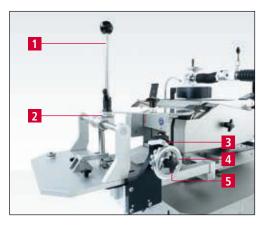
Универсальное устройство для ленточной заточки HV 262
